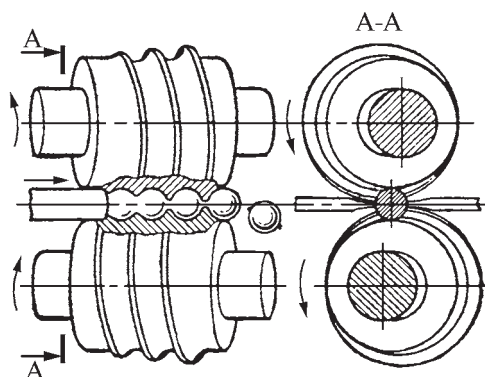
Поперечно-винтовая прокатка в спиральных калибрах
